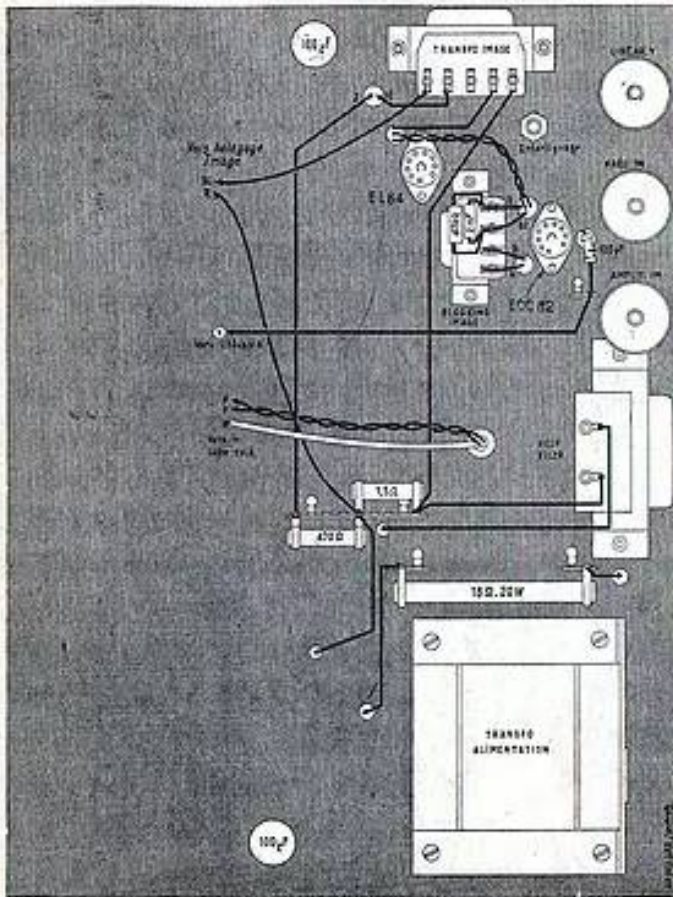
CABLAGÉ DU CHASSIS "B" - FACE INTÉRIÈRE
